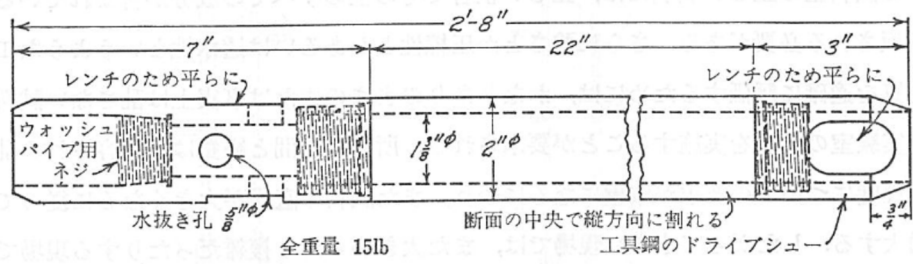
Raymond Concrete Pile 社のレイモンドサンプラーの構造図²⁾
